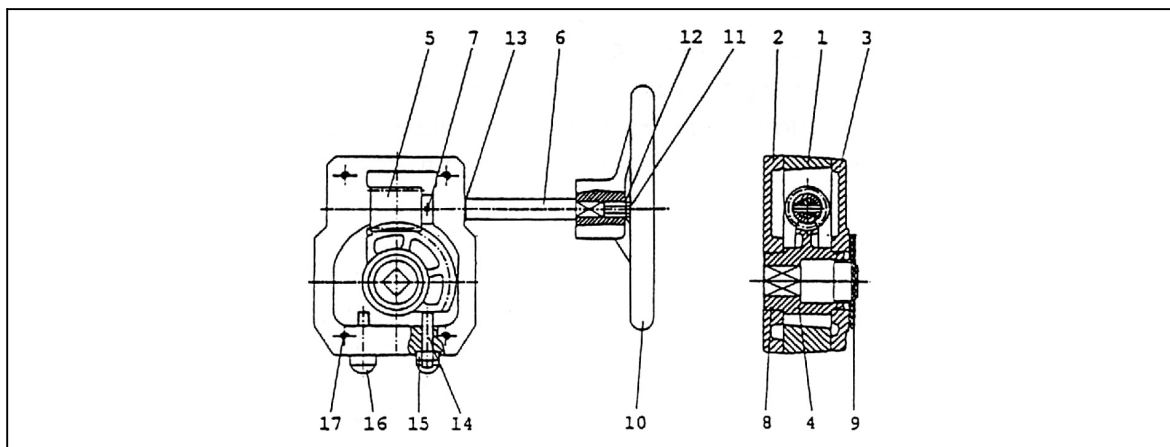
Устройство ручного редукторного привода с червячной передачей RM.
